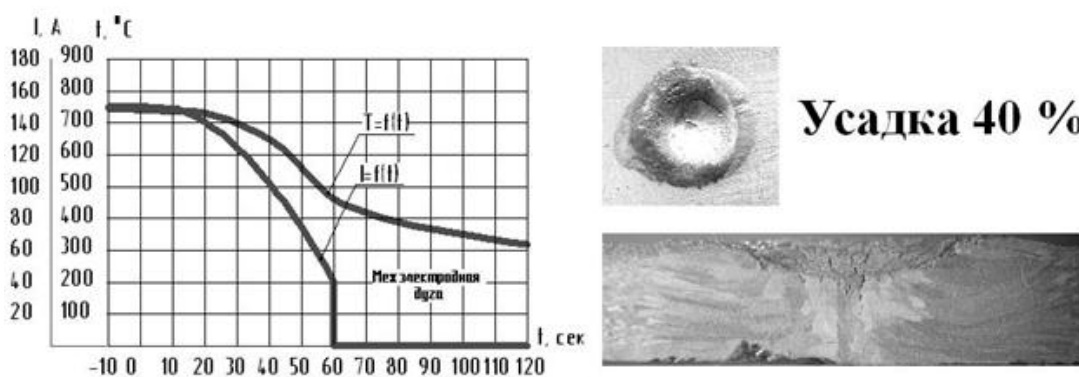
Термический цикл, форма и размеры усадочного кратера при реализации параболической формы кривой спада тока сварки
